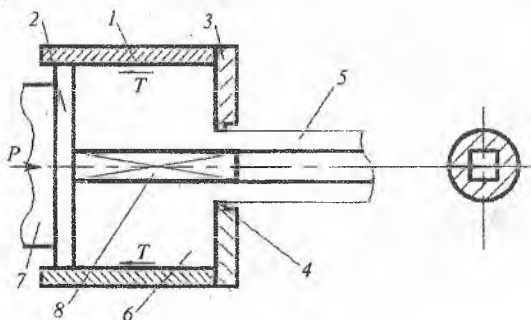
Схема прямого прессования круглой трубы с квадратным отверстием
